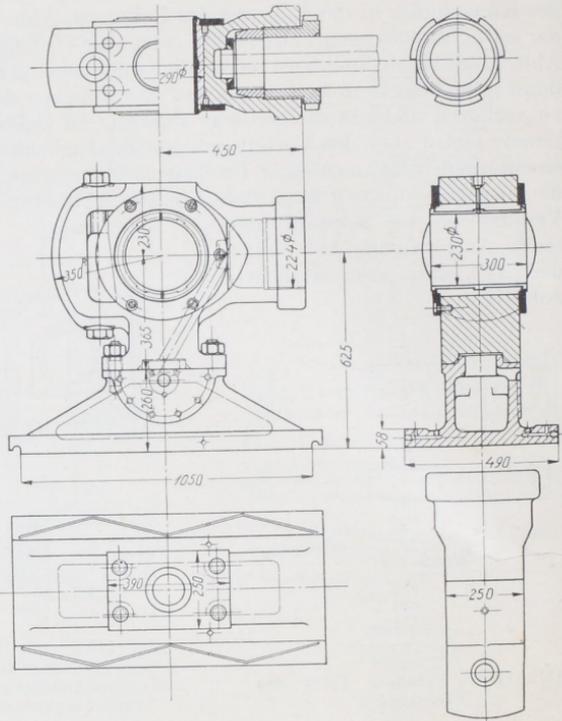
Großgasmaschinenkreuzkopf. Siegener Maschinenbau A.-G., Siegen. M. 1: 20.
